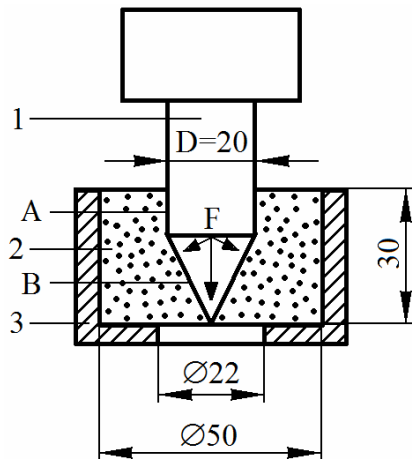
Схема испытания образцов стержневых и формовочных смесей
